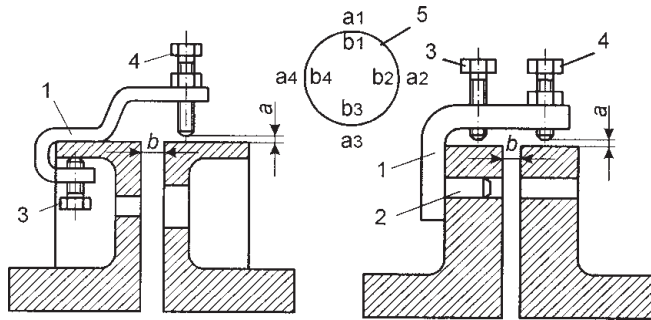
Скобы для центровки электродвигателя с механизмом: *1* — скоба; *2* — палец; *3* — прижимной или стопорный болт; *4* — болт для замера зазора; *5* — рекомендуемая форма записи значений зазоров
